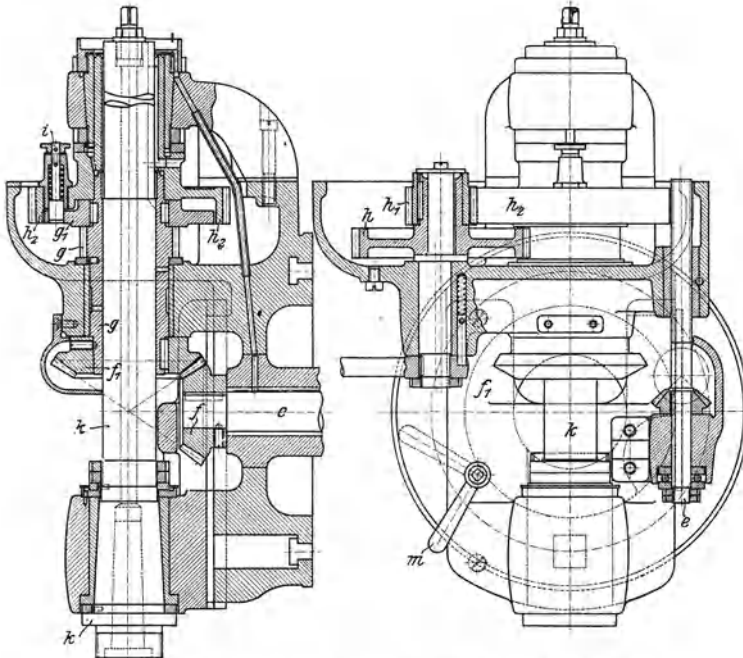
Schnitt und Ansicht des Frässpindelkopfes.
